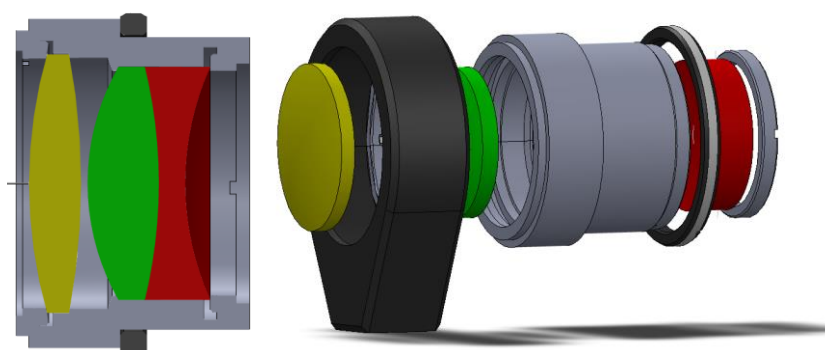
Gauche : vue en coupe du barillet et des lentilles de l'EVF. Droite : vue éclatée de l'ensemble des optiques de l'EVF, avec le support mécanique pour tenir le système sur une table optique.
